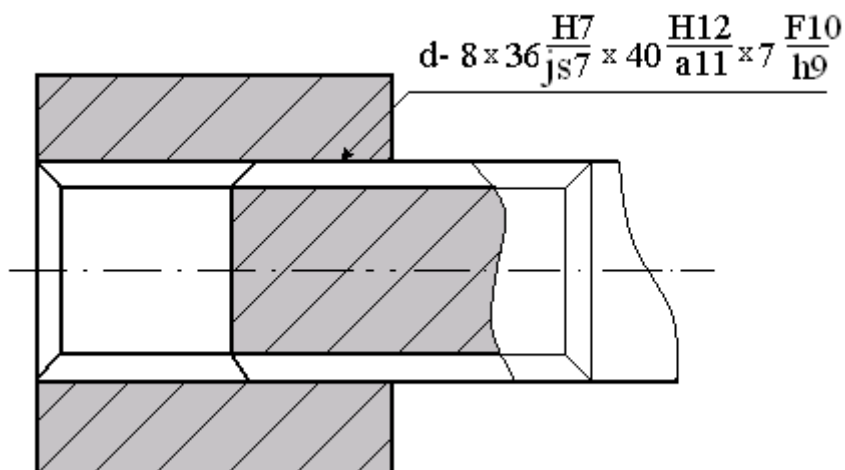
Условное обозначение прямобочного шлицевого соединения на сборочном чертеже
